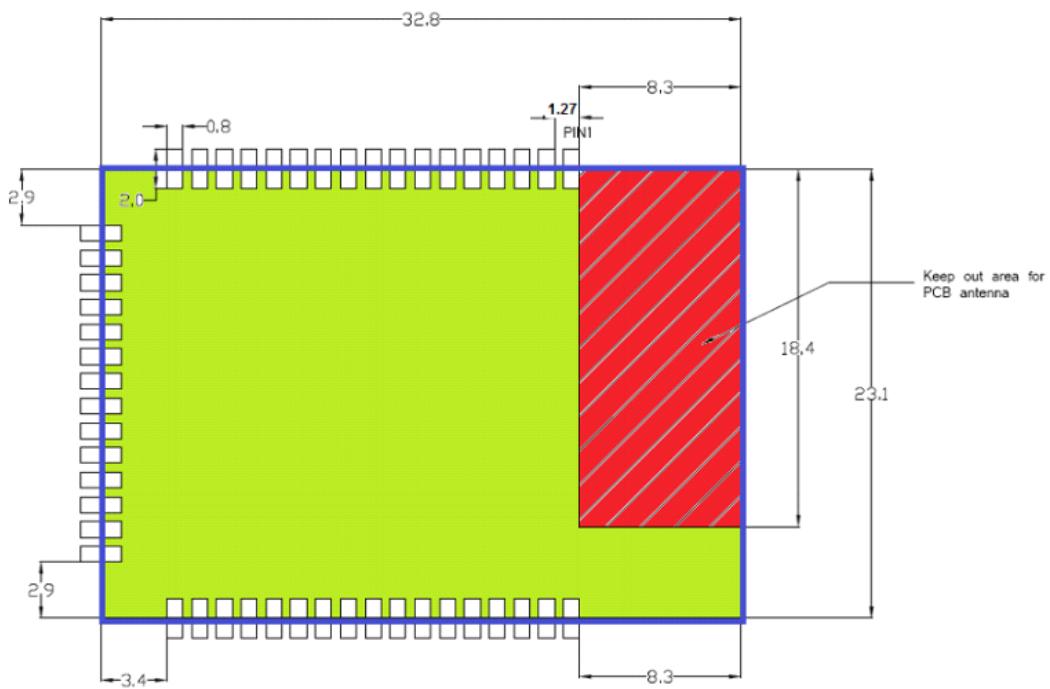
USR-WIFI232-G2/H PCB 元件尺寸
